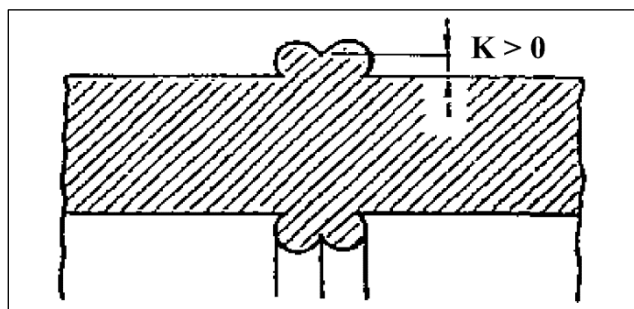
Cordón típico de soldadura a tope de PE
